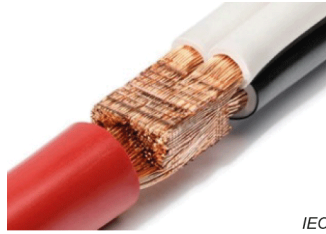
Épissure en ligne cuivre-cuivre, soudée par ultrasons
